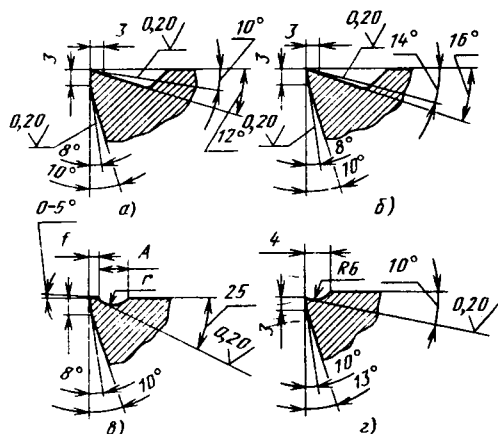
Форма заточки передней поверхности резцов из быстрорежущей стали
